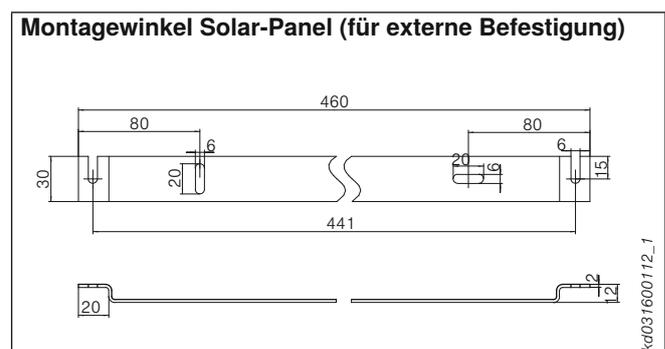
Montagewinkel Solar-Panel (für externe Befestigung)
